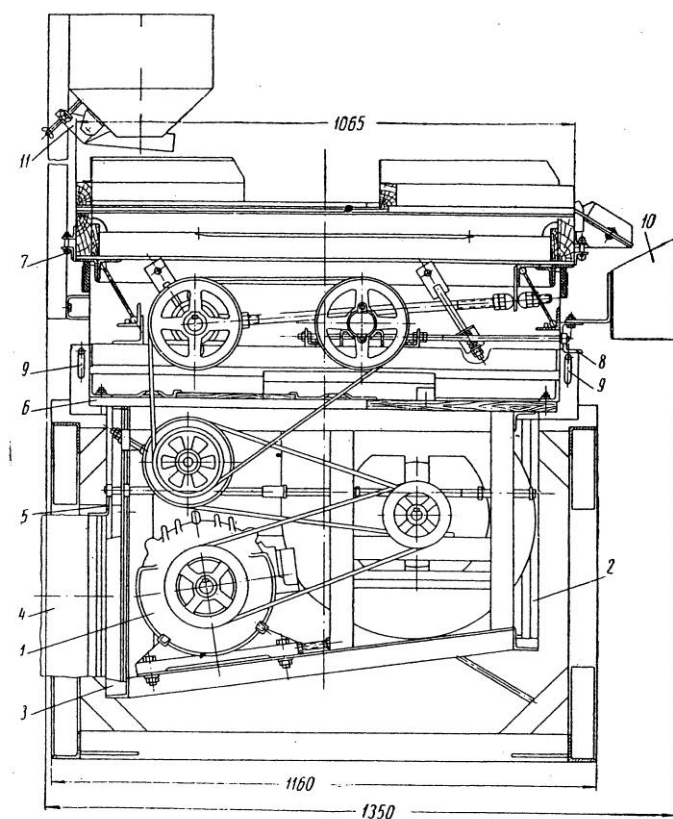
Пневматический сортировальный стол ССП-1,5 (поперечный разрез):
